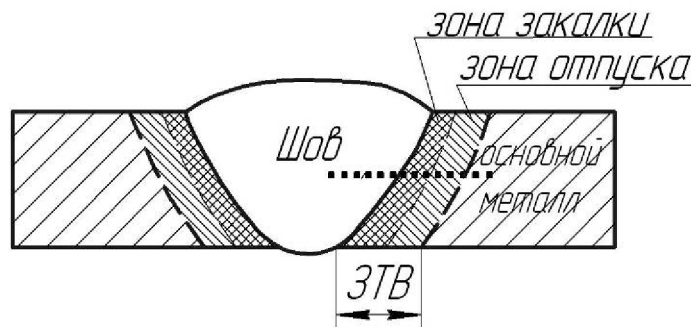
Схема замеров твердости в сварных соединениях броневых сталей
